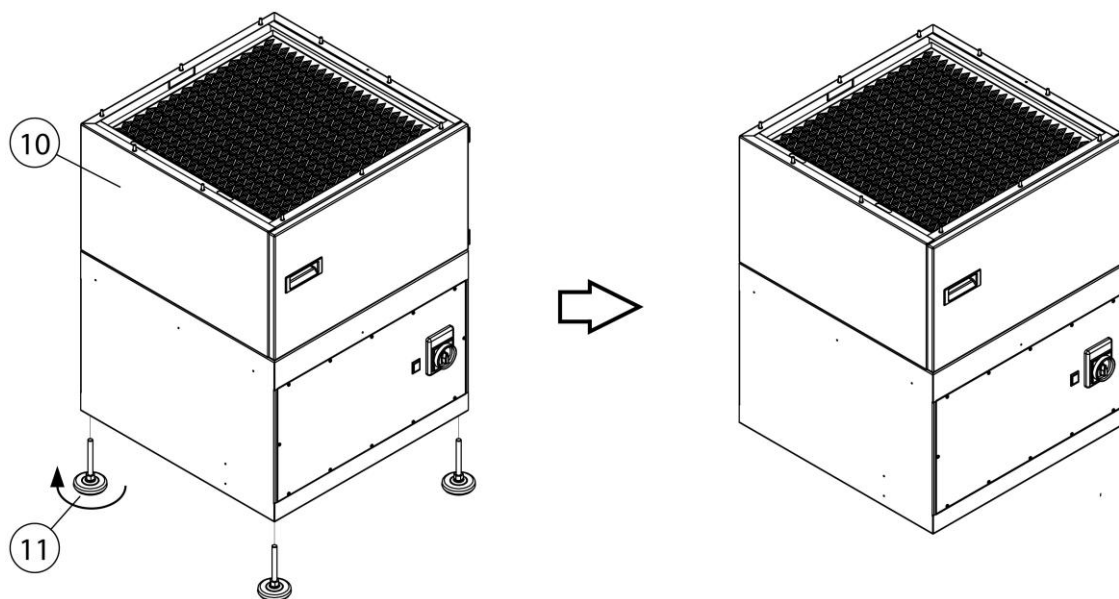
Montaggio - Smontaggio dei piedi di appoggio della macchina
